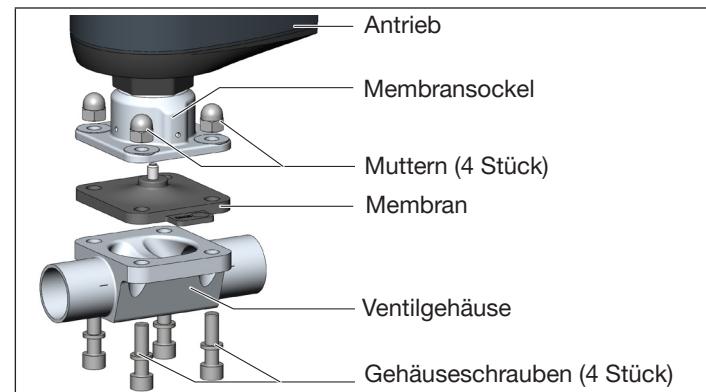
Demontage der Membran am Beispiel 2-Wege-Gehäuse
